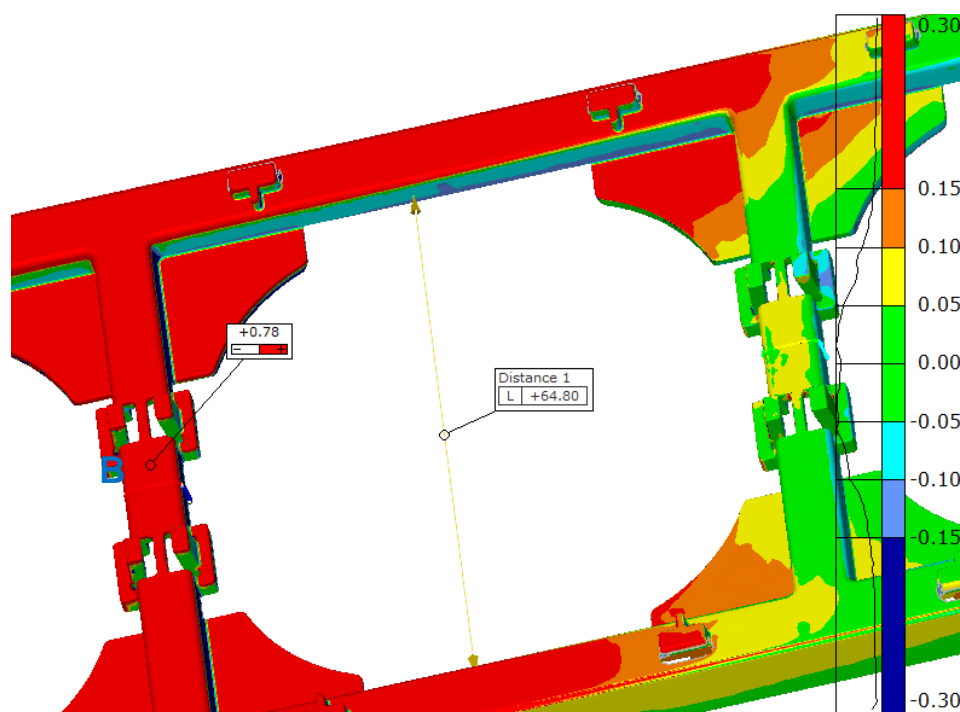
Vizualizace výsledků barevné mapy odchylek od CAD modelu
